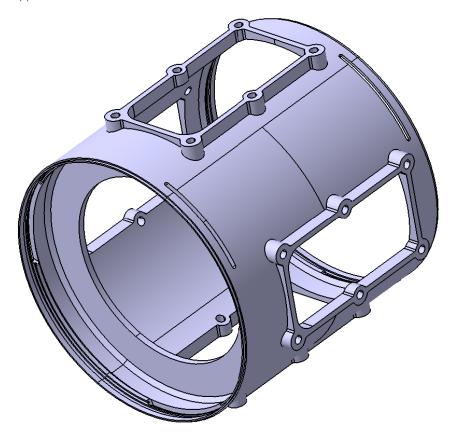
Трехмерная модель детали «Корпус центральный»
